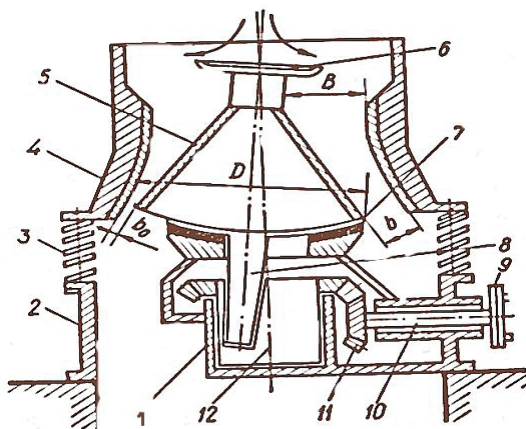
Схема конусной дробилки: 1 — эксцентриковый стакан; 2 — литой корпус; 3 — пружины; 4 — коническая чаша; 5 — дробящий конус; 6 — распределяющая чаша; 7 — опорные кольца; 8 — рабочий вал; 9 — шкив; 10 — приводной вал; 11 — конические шестерни
